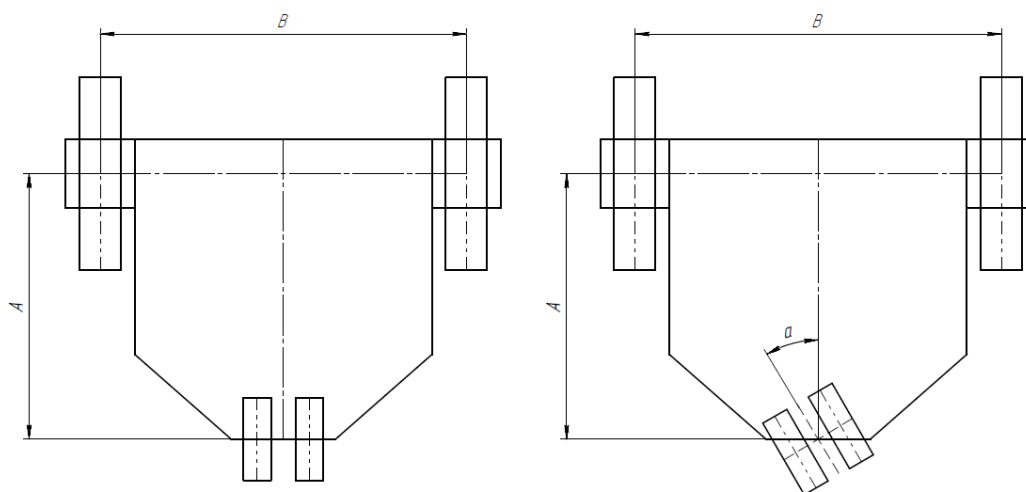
Схема керування з 2-ма приводними та одним опорним колесами
